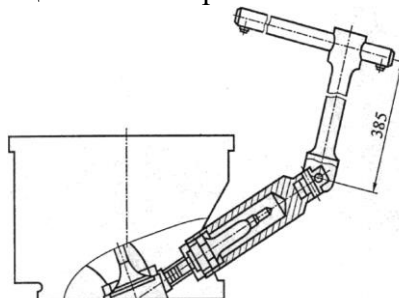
Шарнирный ключ для снятия и установки свечей зажигания и ключ для контроля усилия затягивания свечей зажигания (с отверстием под динамометрический ключ)
